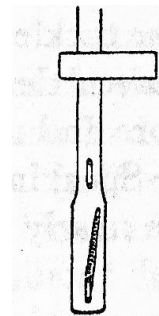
Шпора стеньги со шкивами и пазом для стень-вынтрэпа
